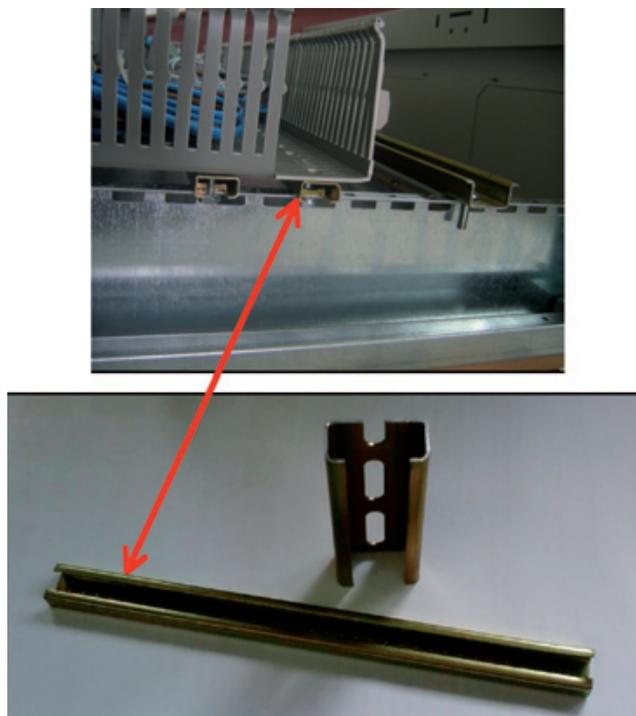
Sistema habitual de colocación de canaletas basado en el empleo de una barra auxiliar
